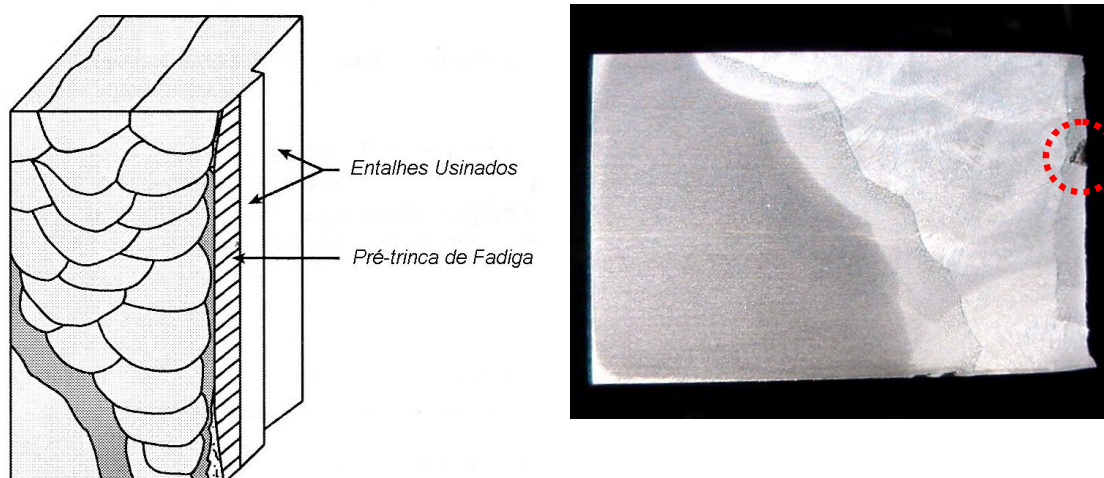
a) Desenho esquemático do seccionamento de uma junta soldada (13); b) macrografia da junta 1/2V soldada, referente ao corpo-de-prova Z23.
